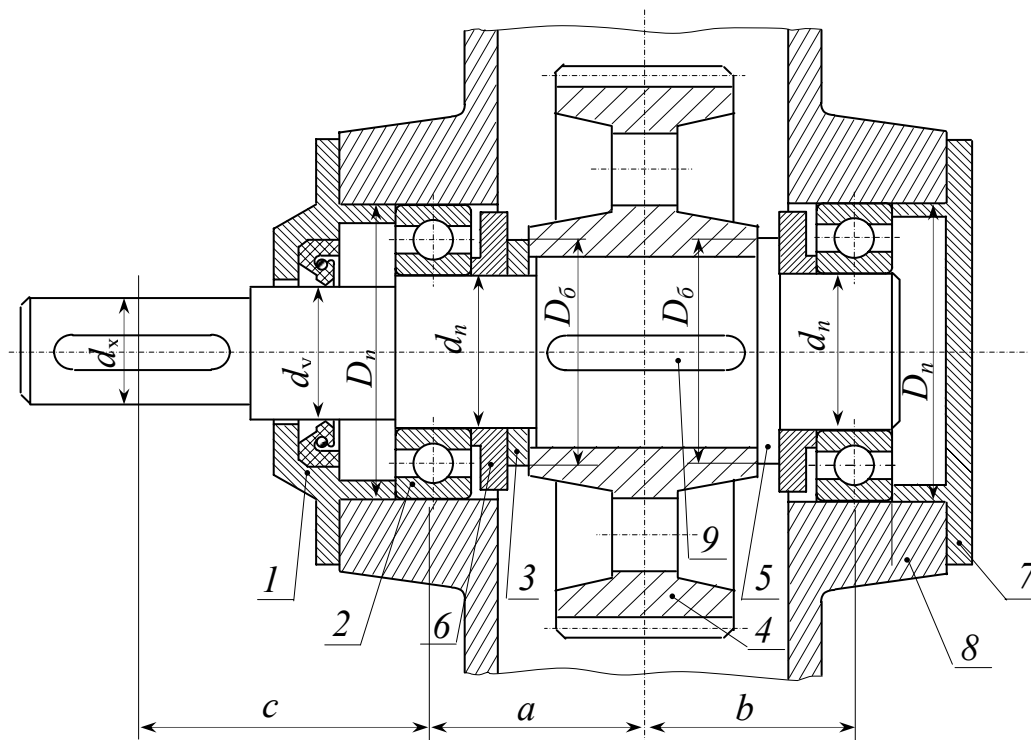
Вузол вала колеса циліндричного одноступінчастого редуктора:
